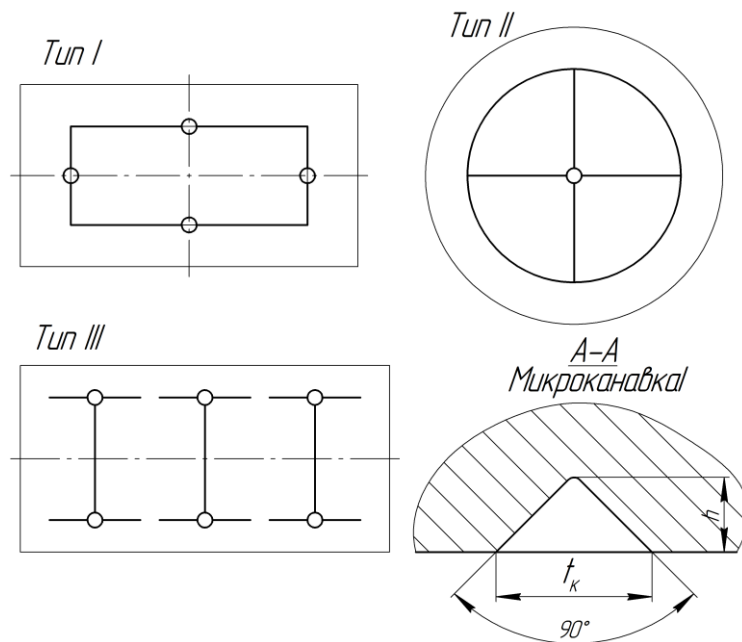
Конструкции и основные размеры прямоугольных и круглых газостатических опор [128]
